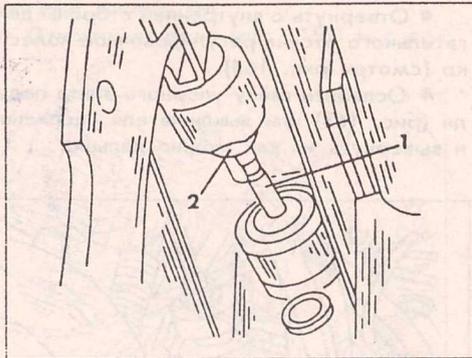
Расположение штока (1) и контргайки (1) на главном цилиндре. Вид с нижней стороны автомобиля.
